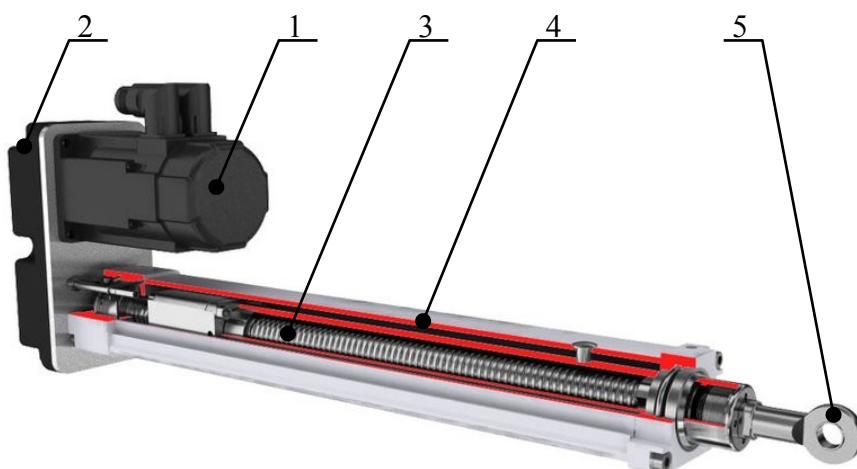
Aktuátor s motorem mimo osu šroubu. Pohyb je transformován pomocí kuželového soukolí ([6])
